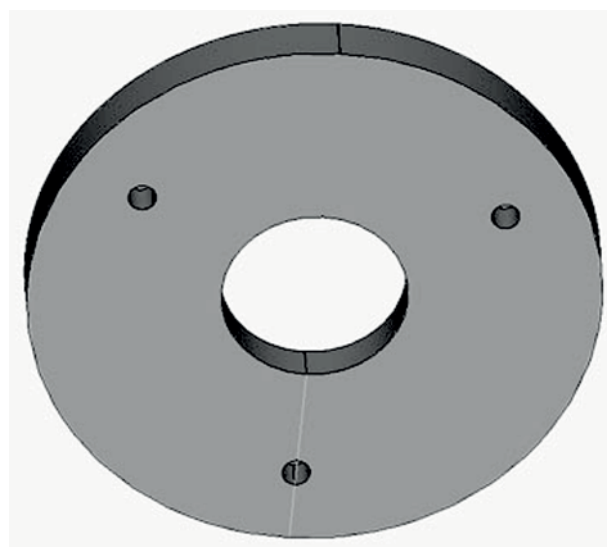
Конструкция двухслойного зеркала из карбида кремния.
